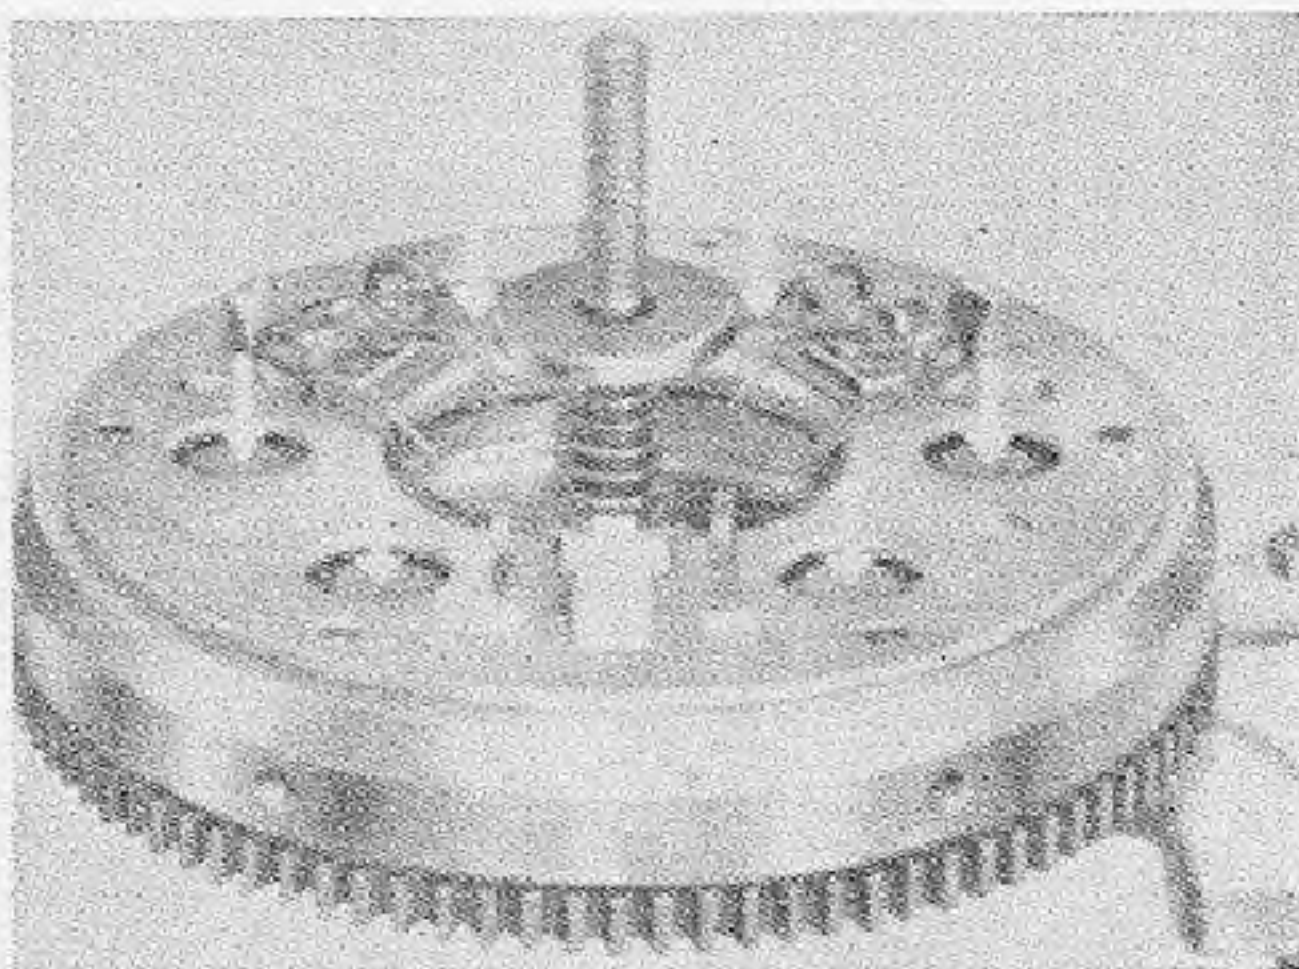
Colocación de las arandelas aislantes con ayuda de la placa de cierre.
